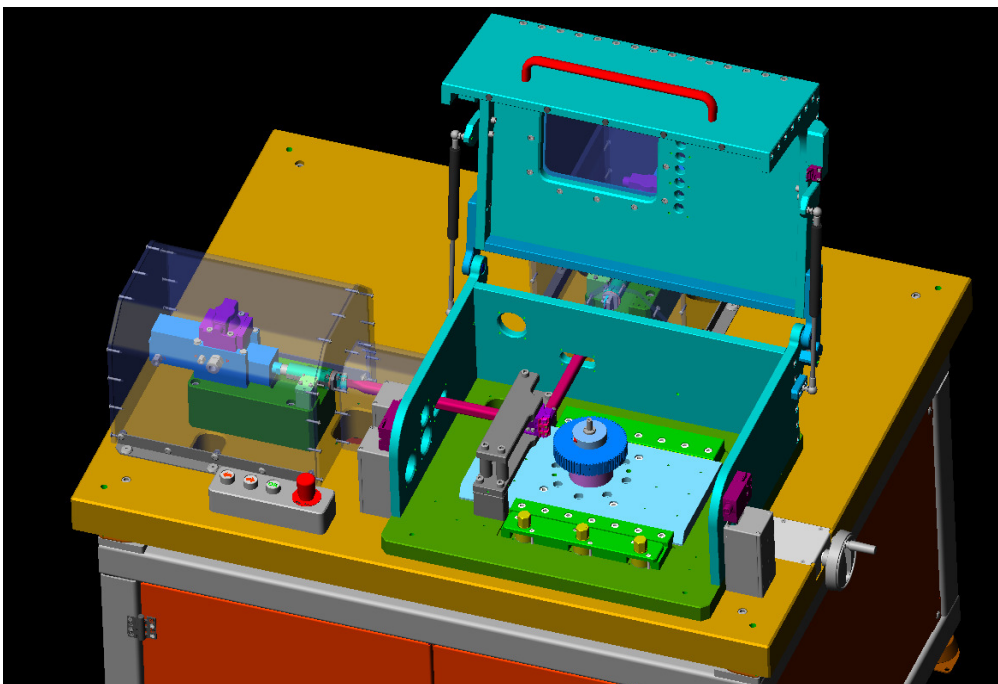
Prüfstand mit geöffneter Schutzkammertür
